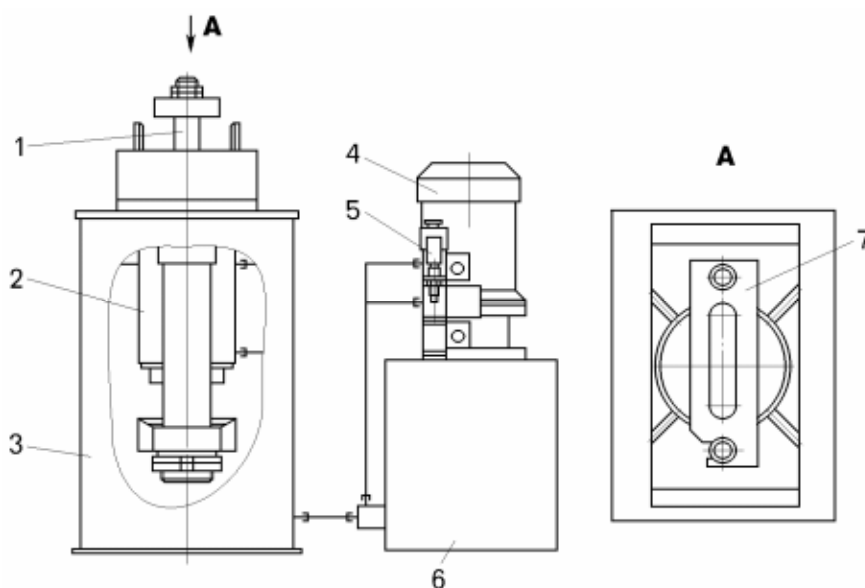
Приспособление для замера натяга манжет цилиндров подвески:
